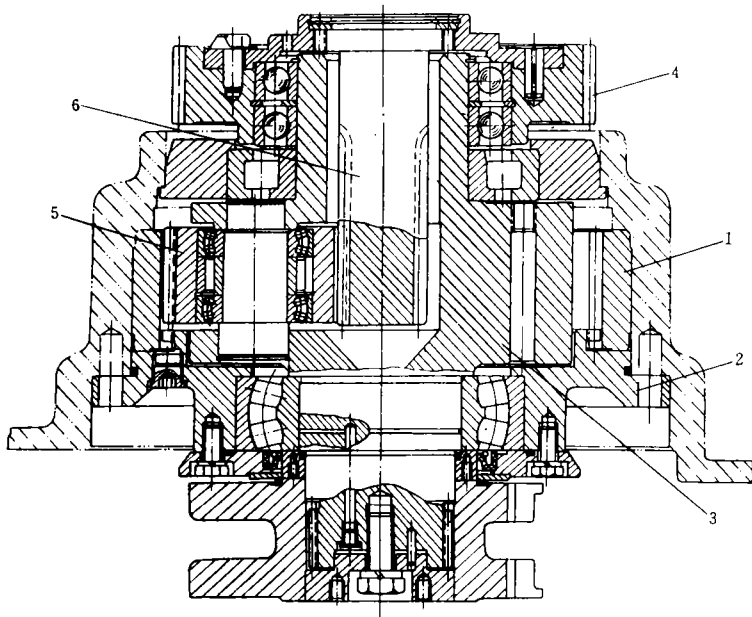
MLS₃-170 型采煤机牵引部行星齿轮传动机构
